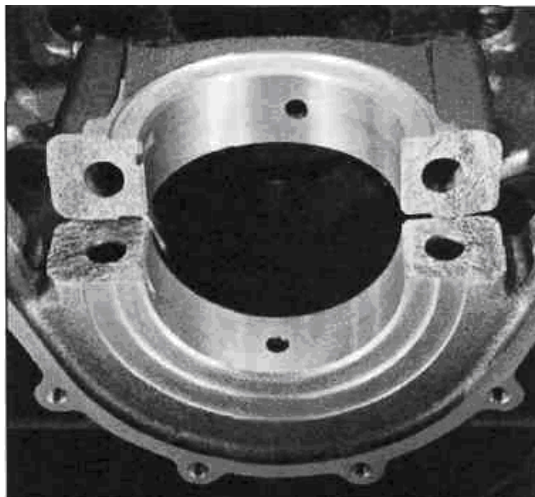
Крышки коренных подшипников коленчатого вала двигателя V8 BMW, изготовленные методом отламывания
